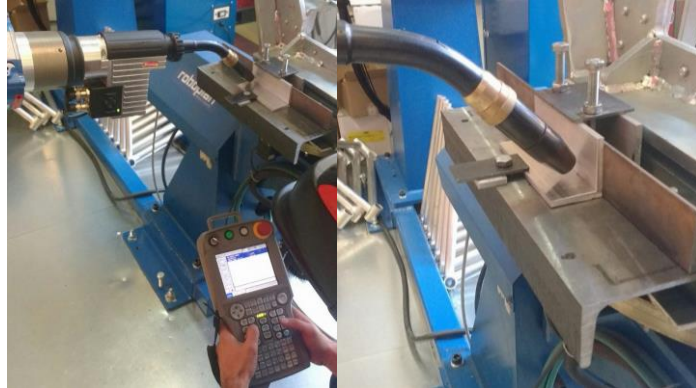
Preparação do posicionamento da tocha de soldadura.
